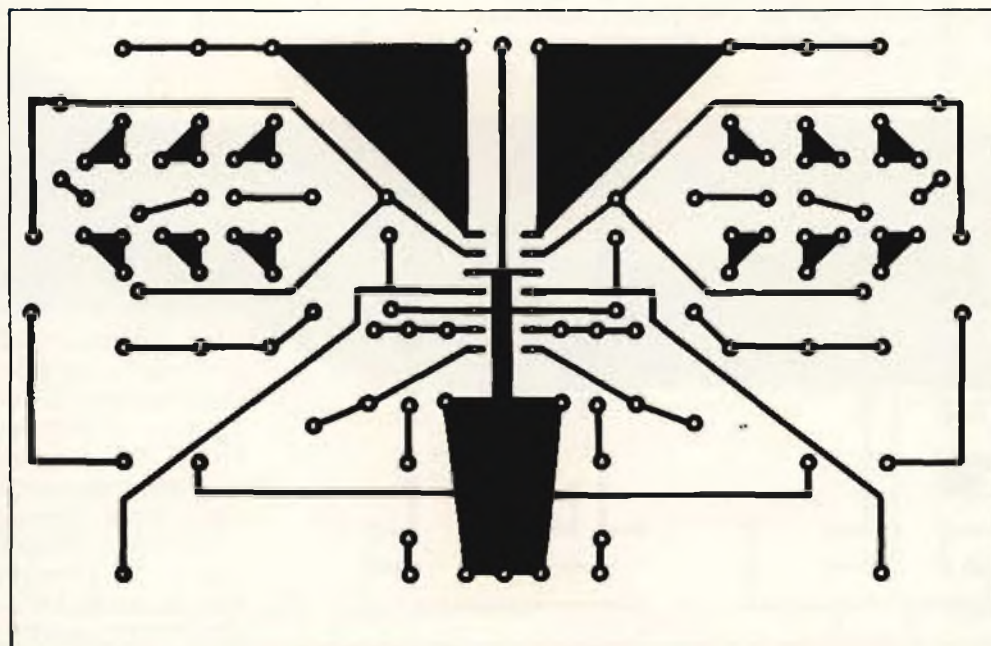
Disegno del circuito stampato dei controlli di tono.
